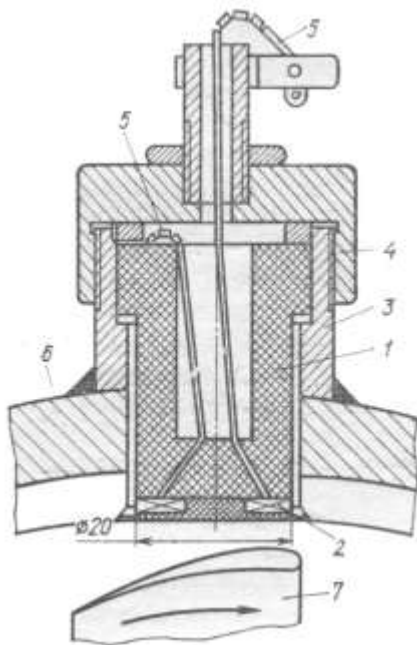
Конструкція неохолоджуваного високотемпературного ВСП для вимірювання робочих зазорів у газотурбінних двигунах: 1 – каркас; 2 – навитка; 3 – корпус; 4 – кришка; 5 – виводи; 6 – статор; 7 – лопатка
